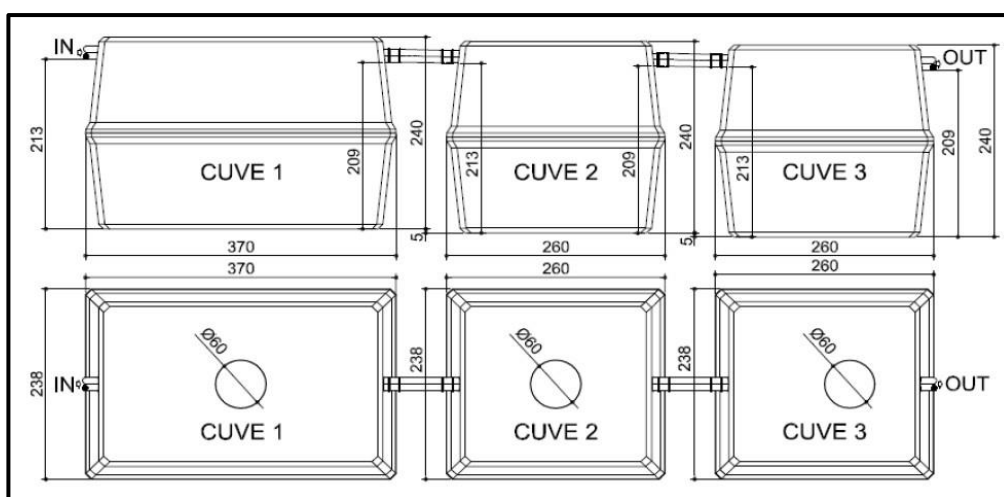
Plan d'encombrement de l'Oxyfix® C-90 CB 58 EH
